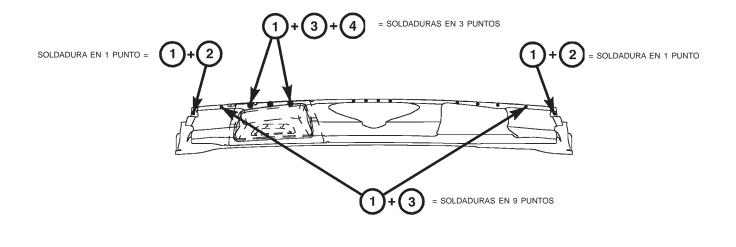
CONJUNTO DE CAMARA IMPELENTE
